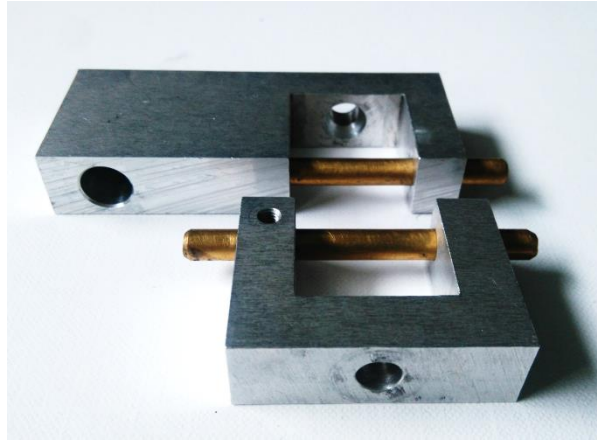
Système d'attache des éprouvettes de la figure 2.18 à la machine d'essai
